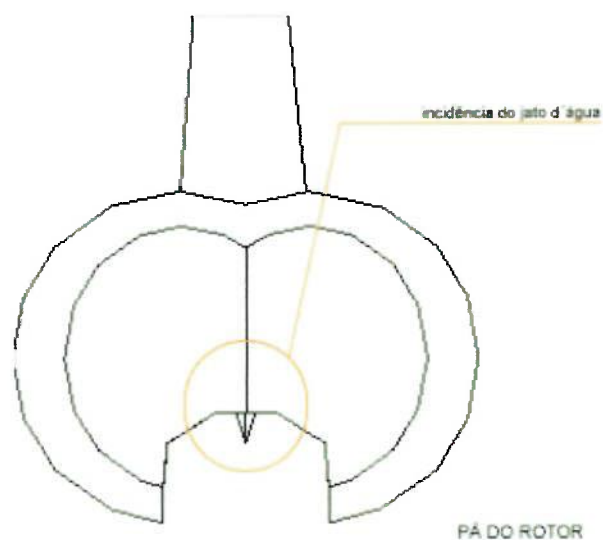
Pá do Rotor de Turbina Pelton. [5]
